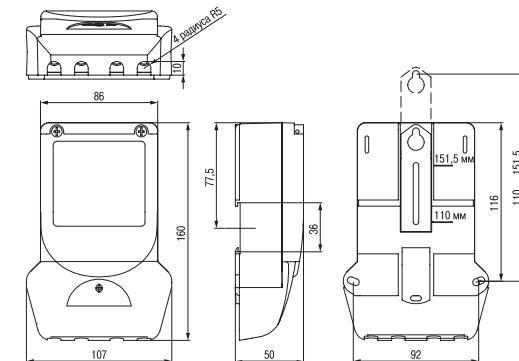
Габаритные и присоединительные размеры счётов габарита корпуса 3.
